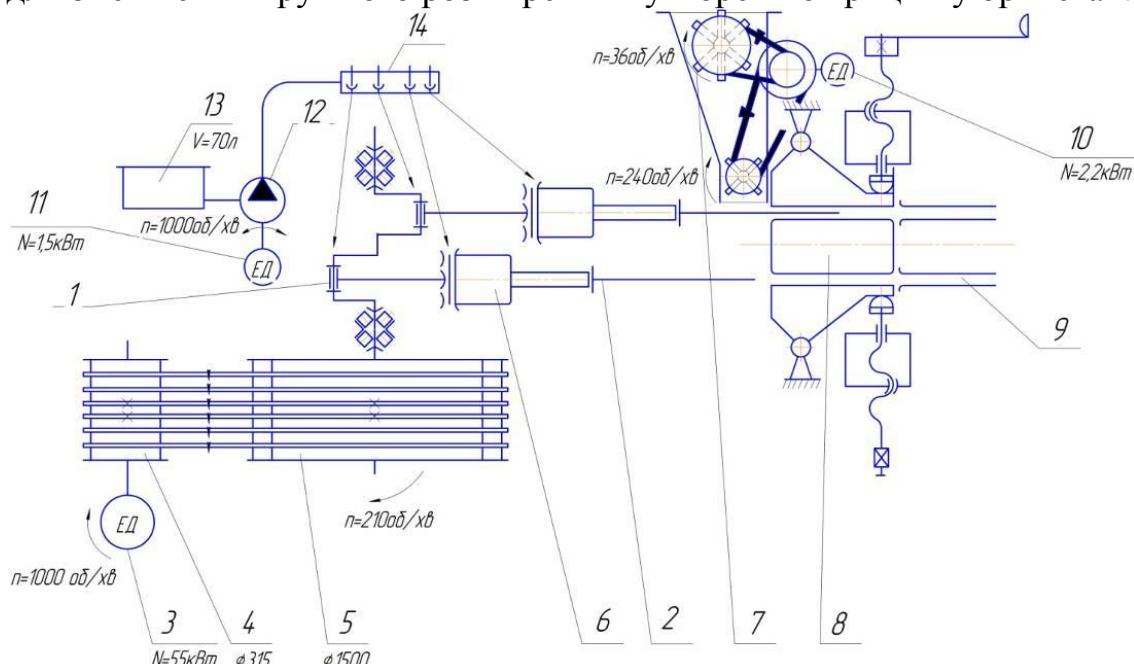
Кінематично-технологічна схема брикетного штемпельного преса: 1 – колінчастий вал; 2 – штемпель; 3, 10, 11 – електродвигуни; 4 – шків; 5 – маховик; 6 – повзун; 7 – живильник; 8 – пресова головка; 9 – лоток; 12 – гідронасос; 13 – гідравлічний бак; 14 – розподільник.
